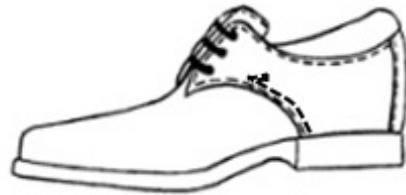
Схема сборки заготовки верха полуботинка с настрочными берцами
